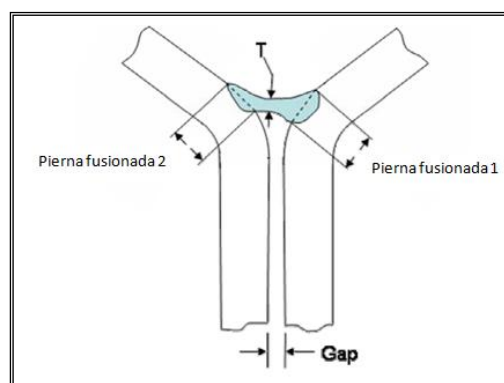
Soldadura de ranura en chasis , ranura en V. ^[1]
